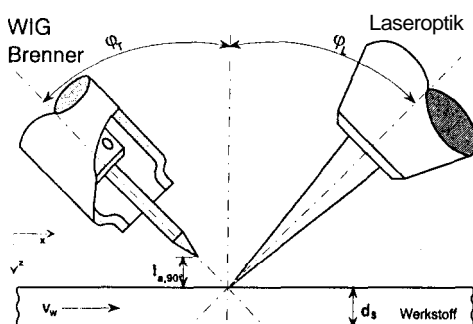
Geometrische Parameter des kombinierten Laserstrahl-WIG-Schweißverfahrens.
